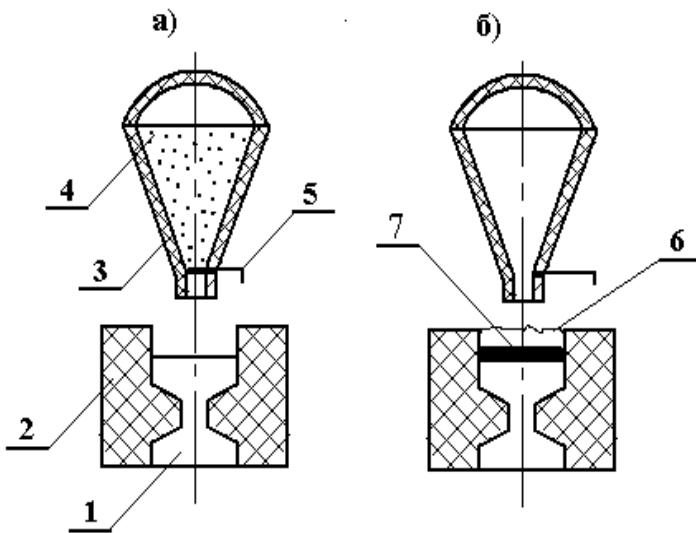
Схема экзотермической наплавки литьем расплавленного металла:
